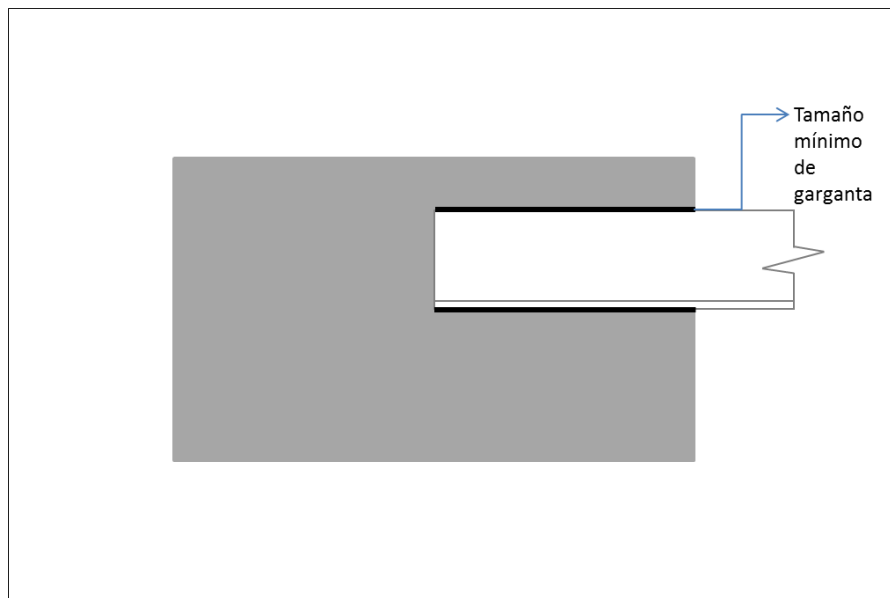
Patrón de soldadura utilizado en el caso 1.
